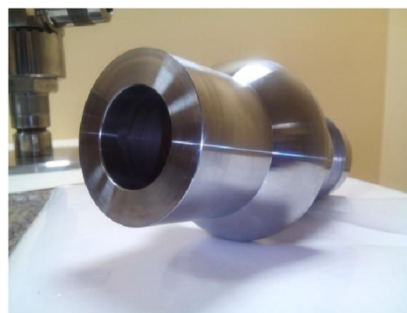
Фото патрубка клапана высокого давления, упрочненного наплавкой, после финишной обработки контактной поверхности (перед сборкой)
